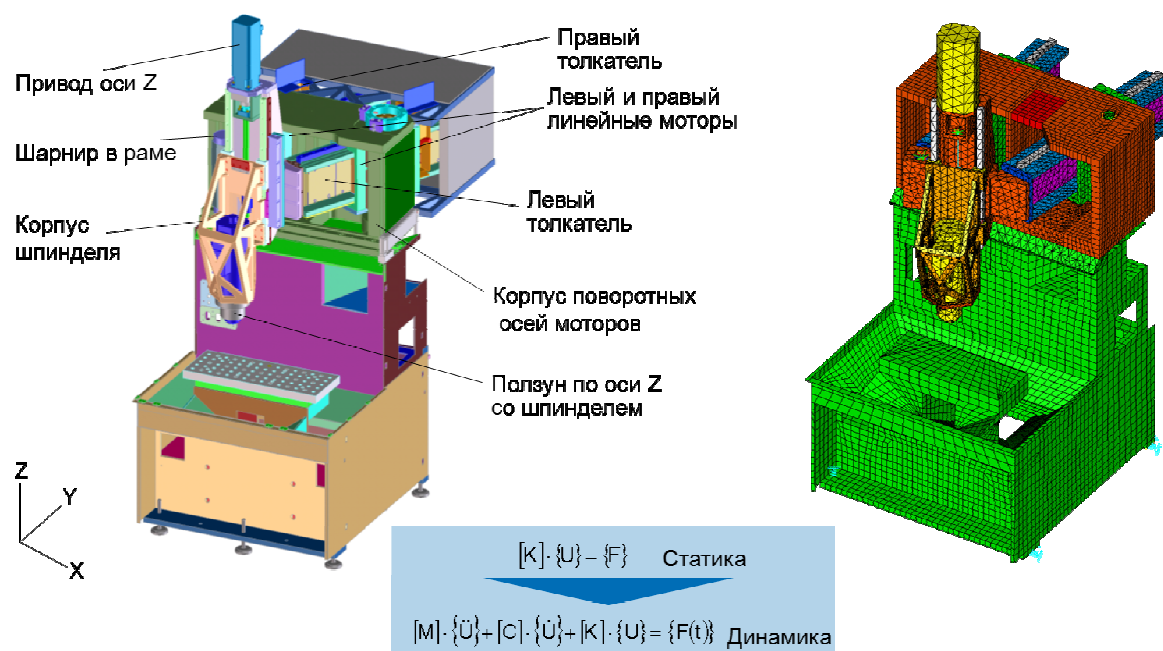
Геометрическая и КЭ-модель фрезерного станка
